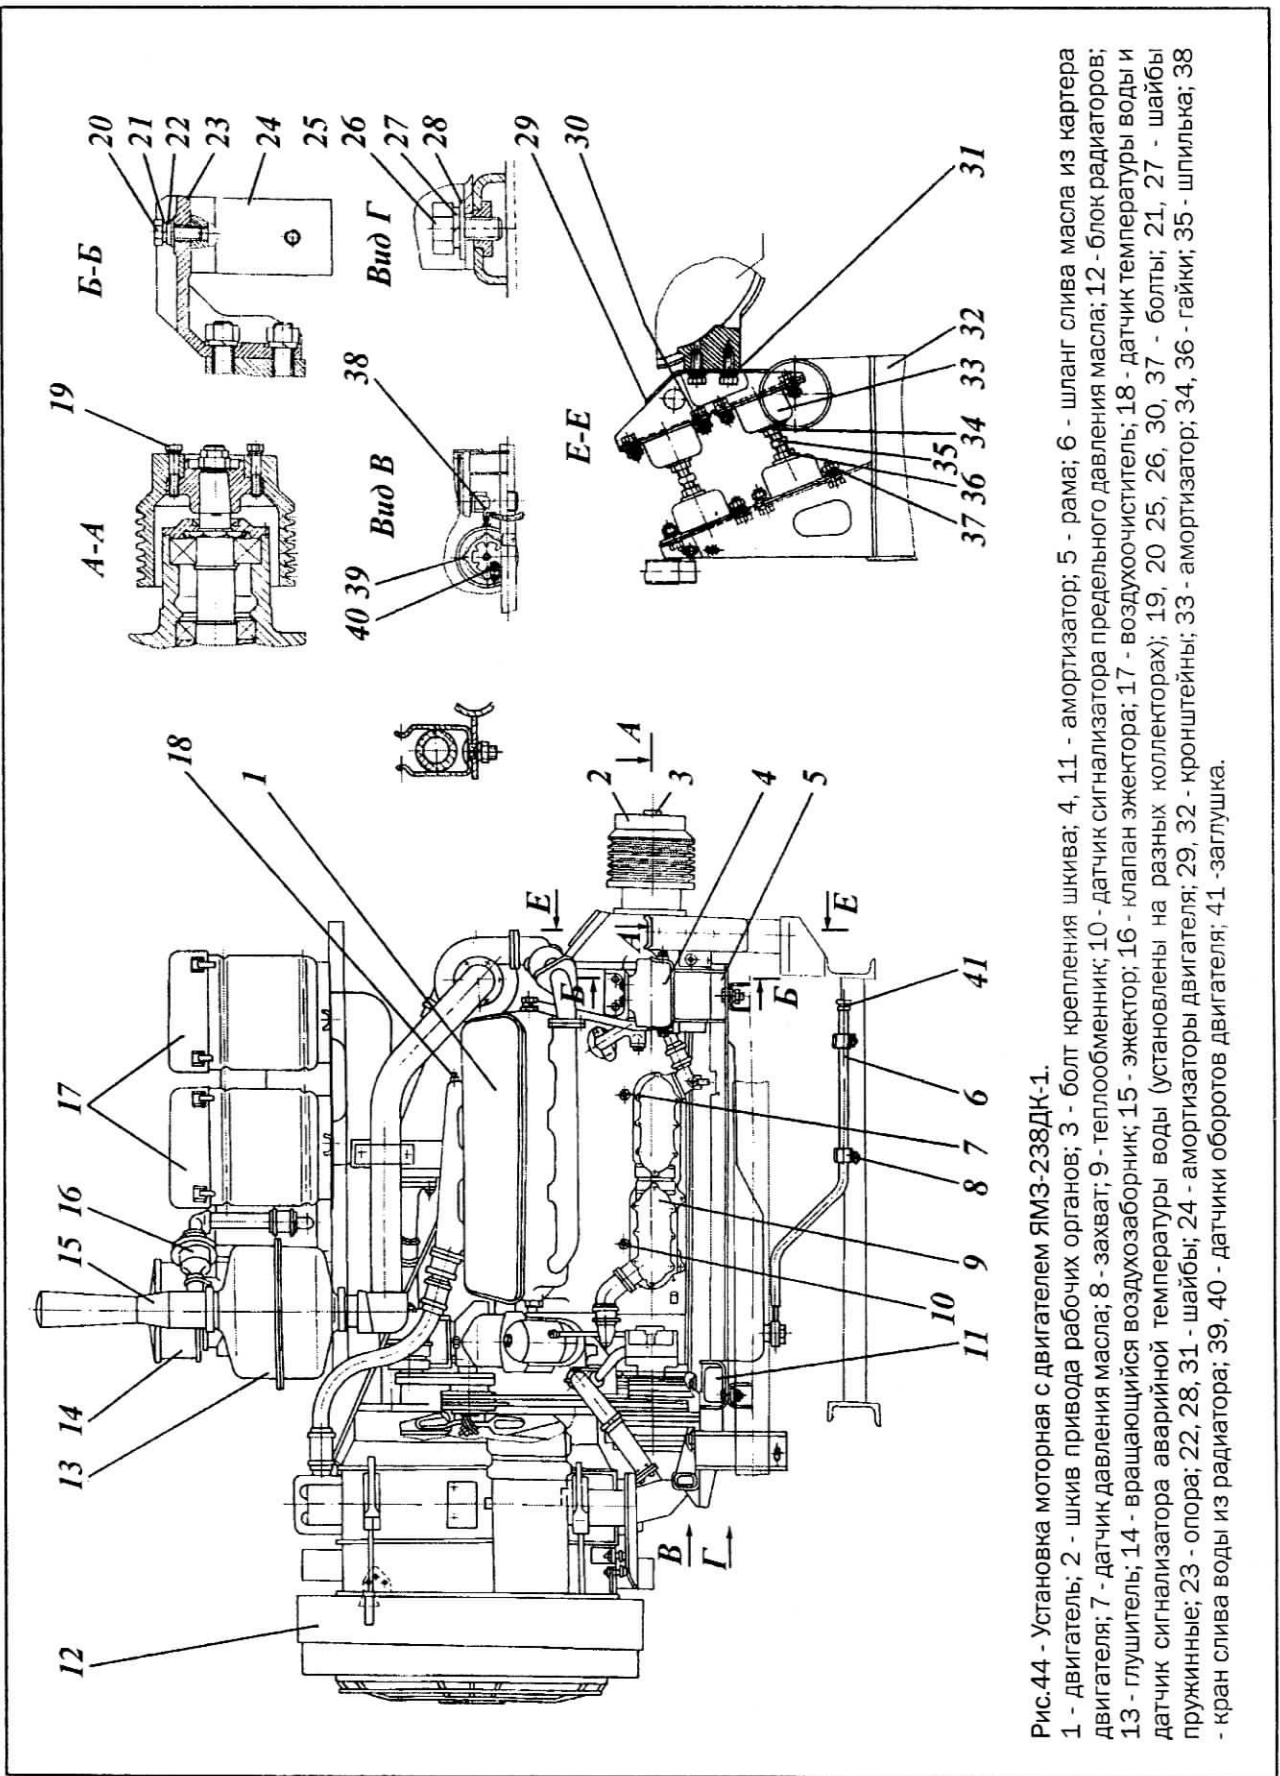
Установка моторная с двигателем ЯМЗ-238ДК-1.
